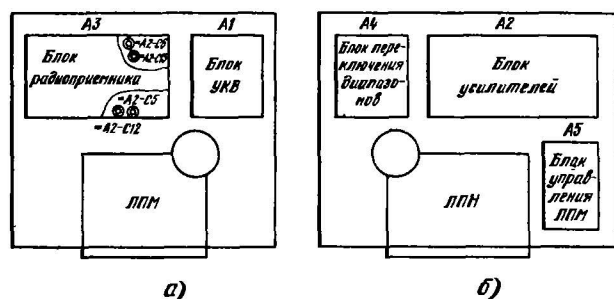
Схема расположения основных блоков и узлов в корпусе автомагнитолы «Золa PM-320CA»: а — вид сверху; б — вид снизу
